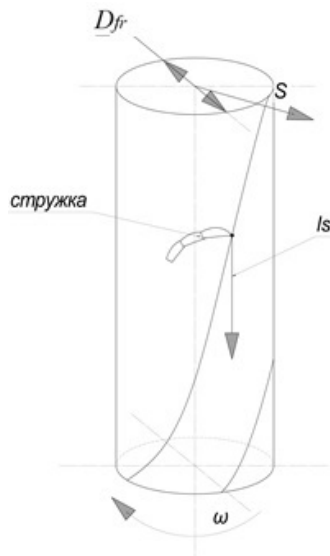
Секундное перемещение зоны контакта с обрабатываемой поверхностью по режущей кромке фрезы
